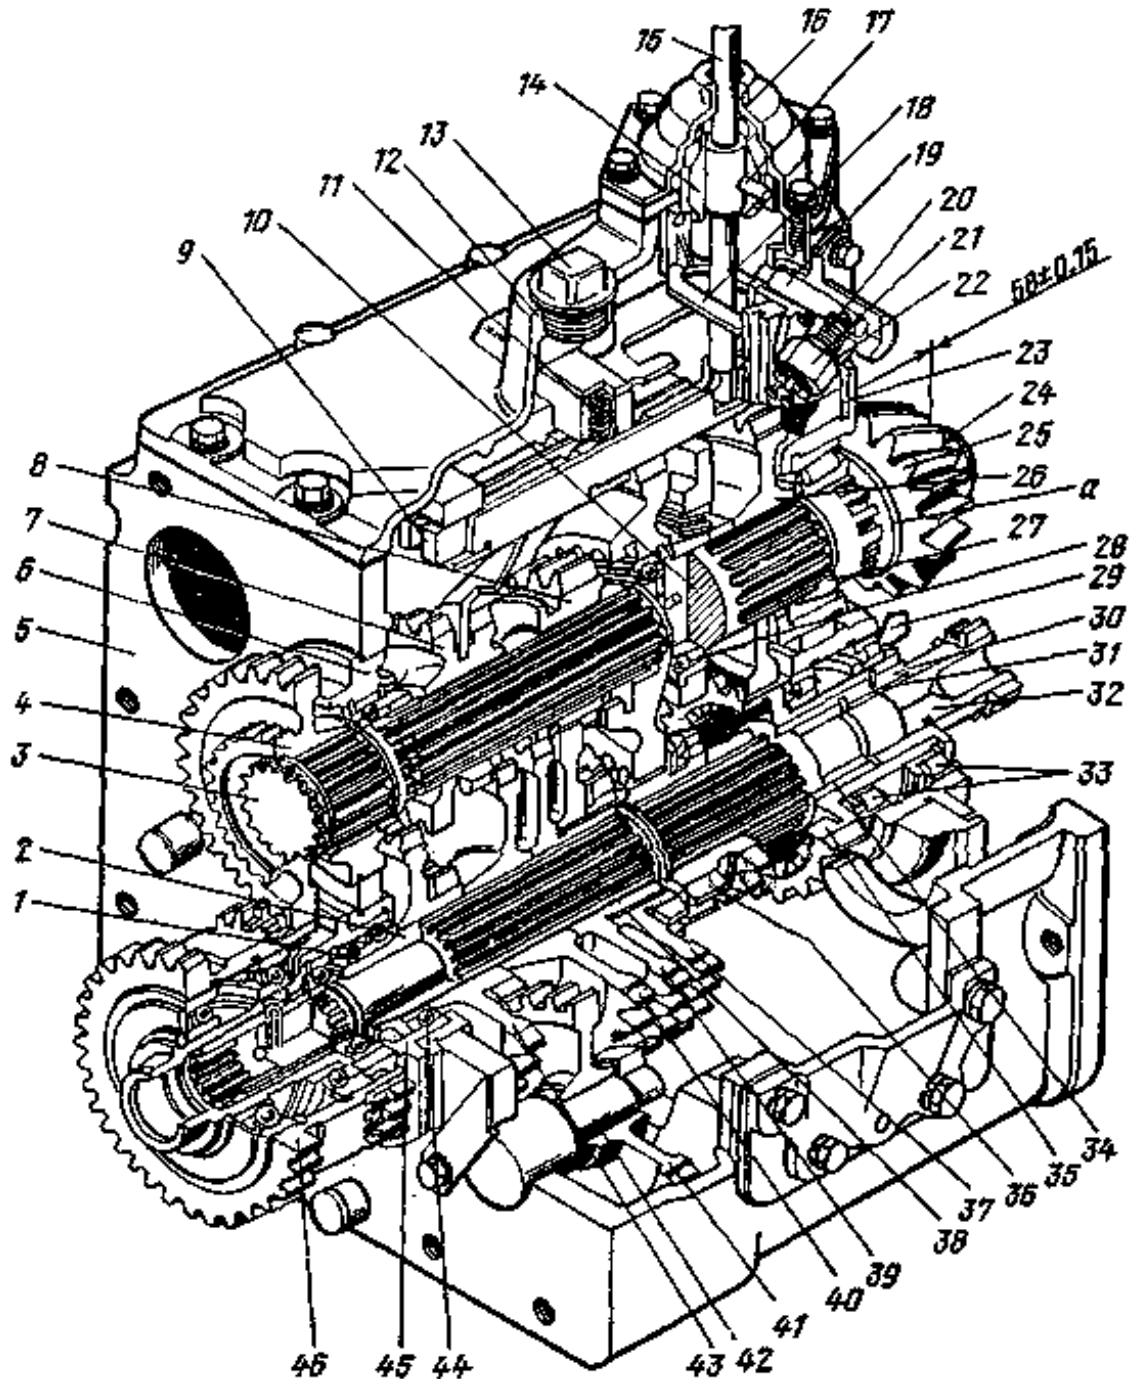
Типова коробка передач трактора ХТЗ:
